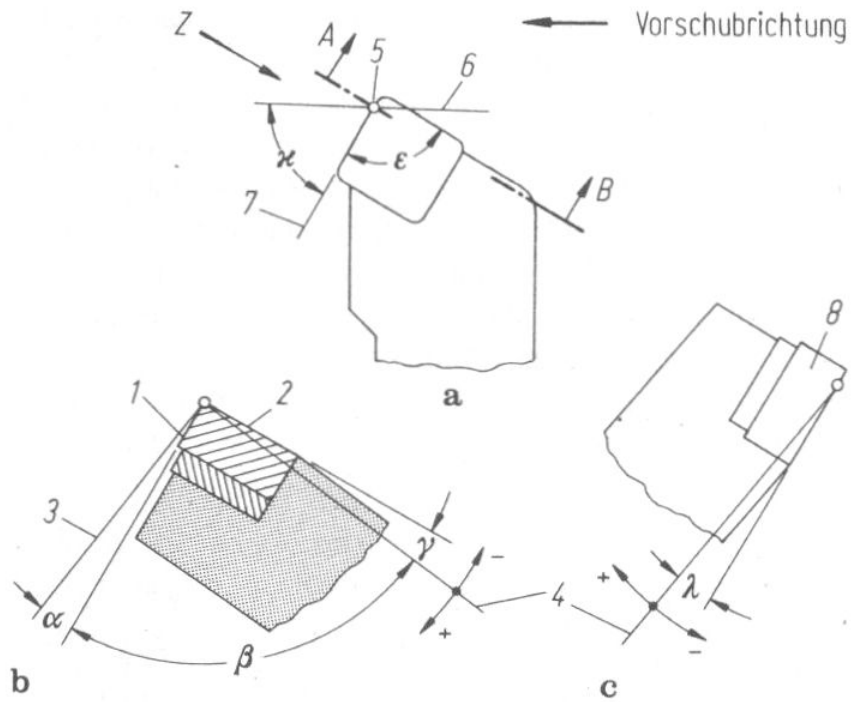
c. Winkel am Drehwerkzeug (DIN 6581).
